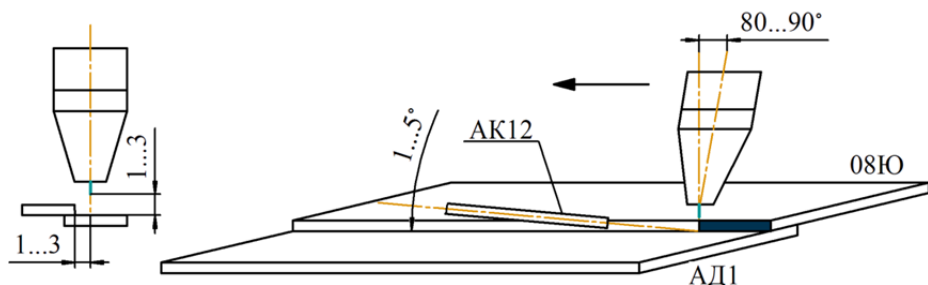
Схема TIG сварки пайки с присадочной проволокой [14]
